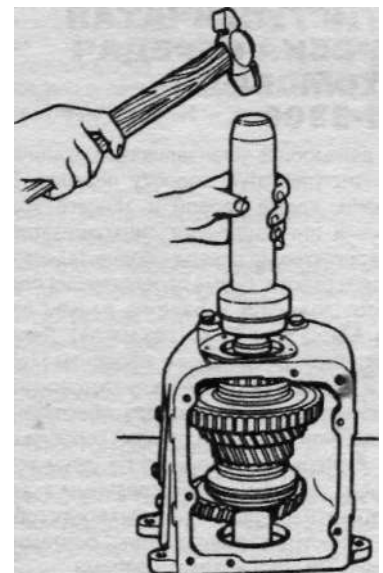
Запрессовка шарикового подшипника вторичного вала
